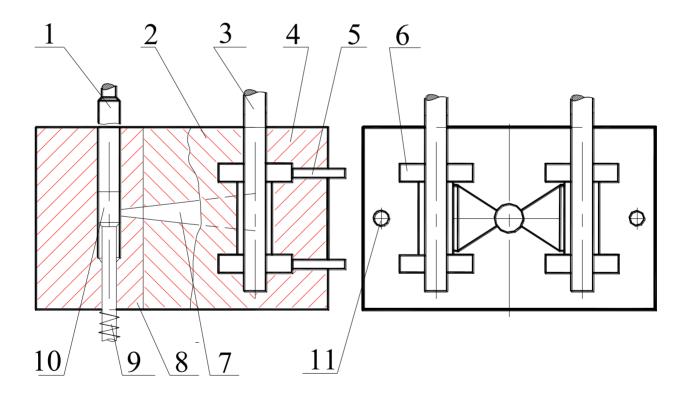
Пресс — форма для литья под давлением с вертикальной холодной камерой прессования: 1 — верхний прессующий поршень, 2 — полуформа неподвижная, 3 — стержень металлический, 4 — полуформа подвижная, 5 — толкатель, 6 — рабочая полость формы, 7 — литниковая система, 8 — камера прессования, 9 — пружина, 10 — нижний выталкивающий поршень, 11 — отверстие центрирующее
